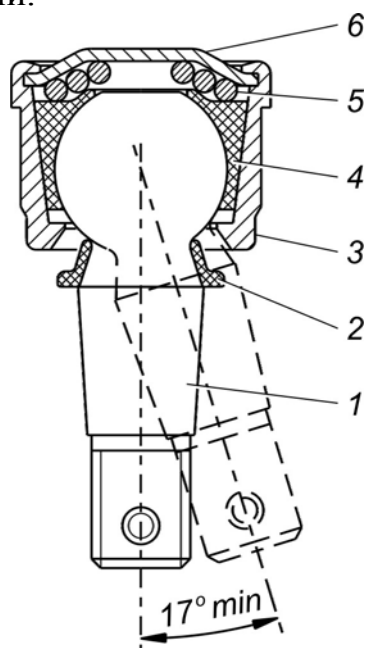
Шарнир рулевых тяг: 1 – палец; 2 – корпус; 3 – вкладыш; 4 – пружина; 5 – крышка
